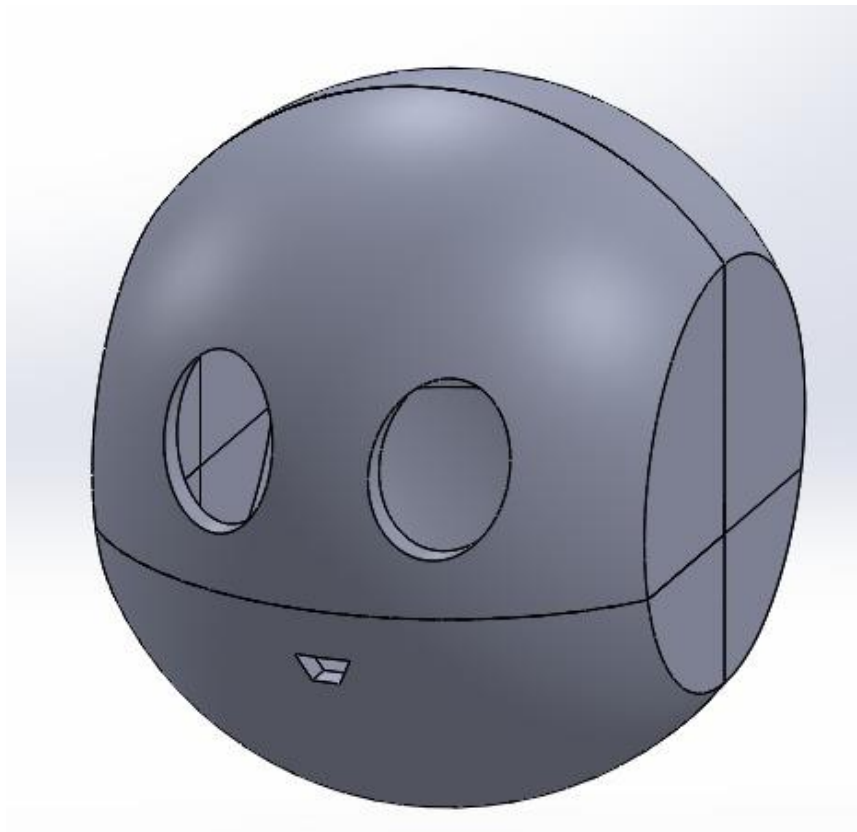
vista isométrica (3D) del diseño de la cabeza robótica.
